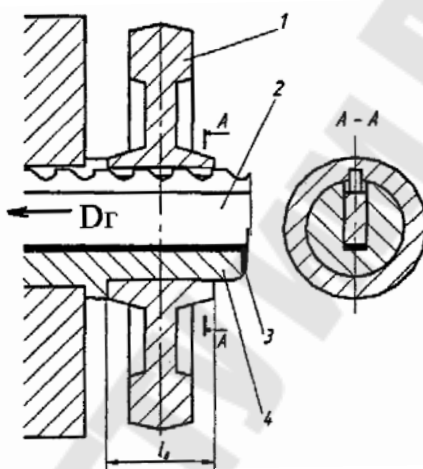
Протягивание шпоночного паза в отверстии
